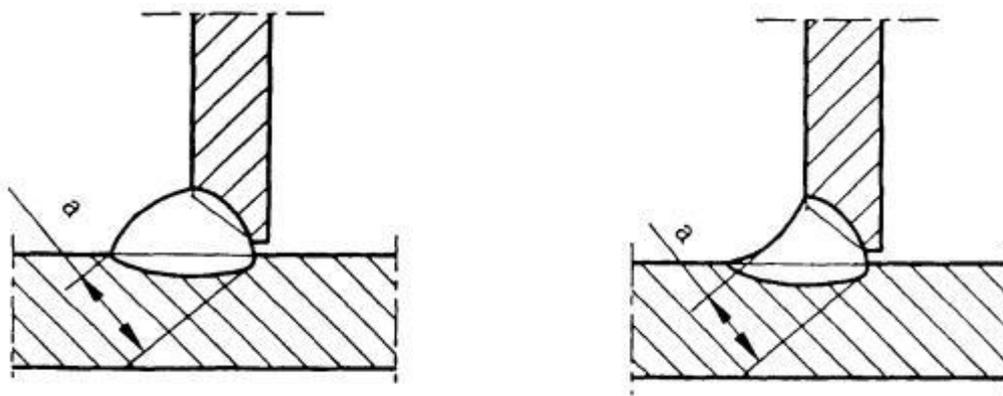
Вогнутость в сварном соединении
